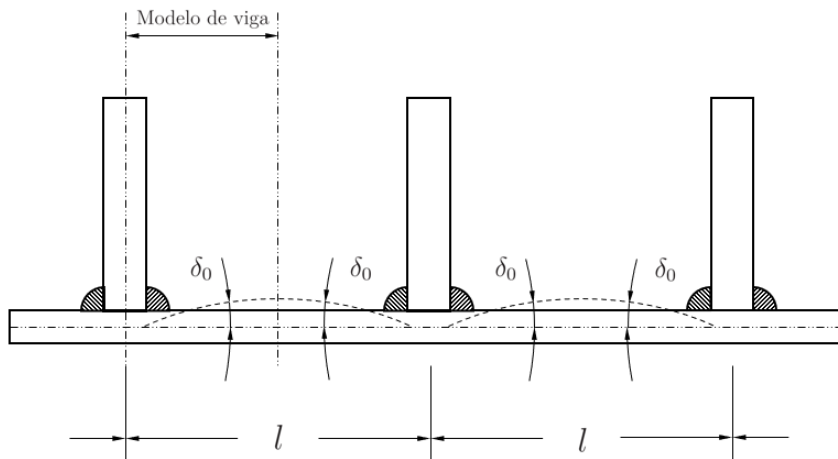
Deflexión de la placa inferior entre refuerzos debido a soldadura de filete. [15]
